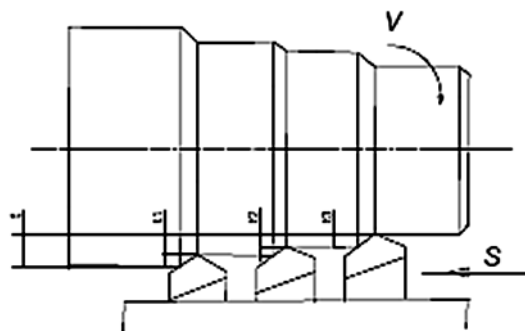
Обработка заготовки методом разделения припуска тремя резцами
